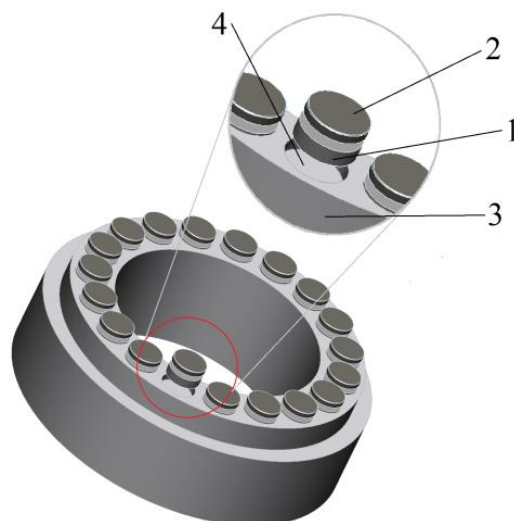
Конструкция упорного подшипника: 1 – подложка из карбида вольфрама, 2 – слой поликристаллического алмаза, 3 – кольцо-основание из нержавеющей стали, 4 – соединение пайкой
